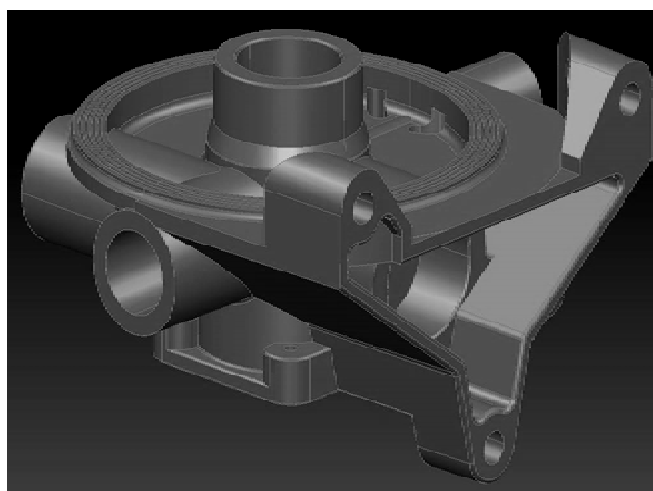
Литая заготовка и модель детали «Корпус адсорбера».
